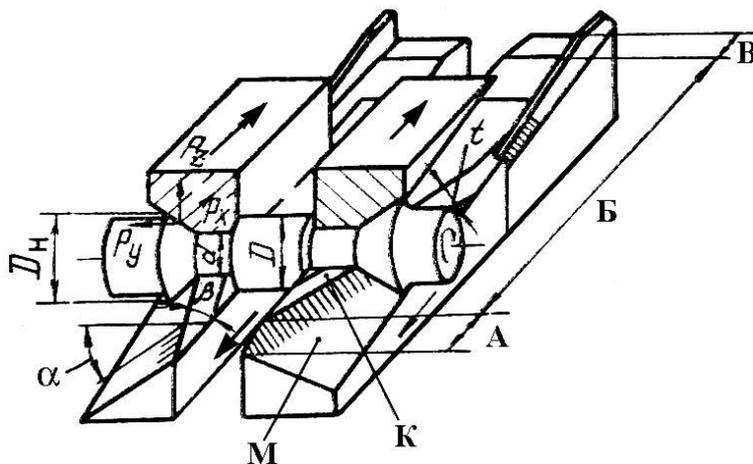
Типовой инструмент плоской поперечно-клиновой прокатки
